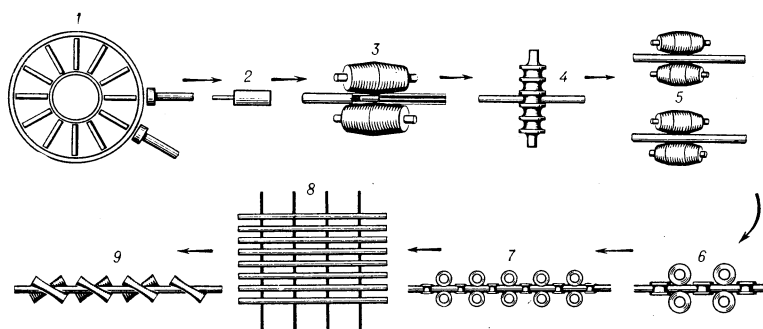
Схема технологического процесса производства труб на трубопрокатном агрегате с короткооправочным удлинительным станом: 1 — нагрев исходной заготовки; 2 — центровка заготовки; 3 — прошивка на прошивном стане; 4 — раскатка на короткооправочном стане; 5 — раскатка на раскатных станах; 6 — прокатка на калибровочном стане; 7 — прокатка на редуционном стане; 8 — охлаждение готовых труб; 9 — правка труб на косоуальных правильных машинах.
